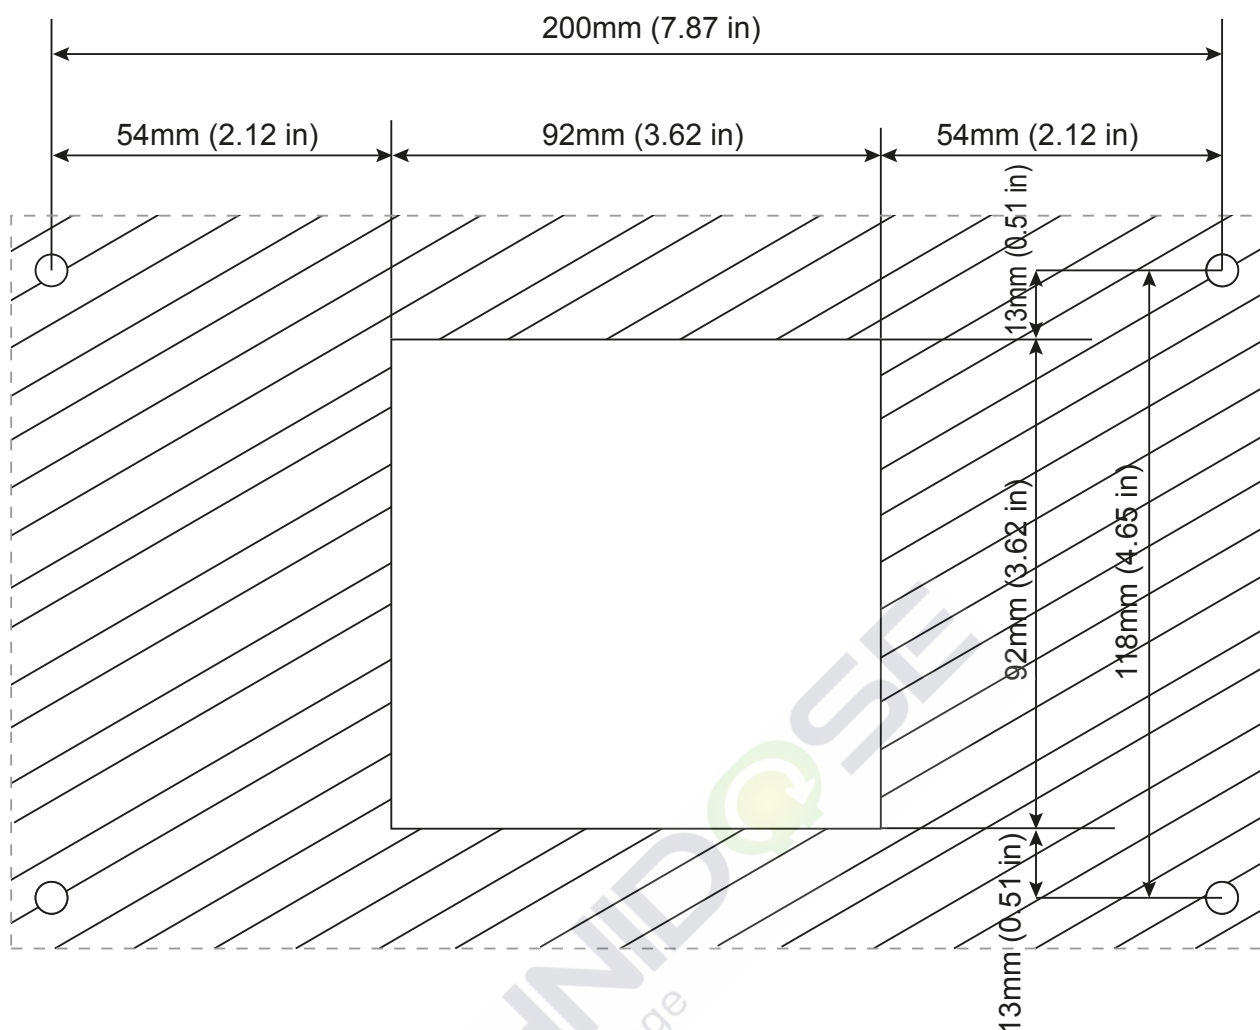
Découpe et dimensions du panneau pour dispositif monté sur panneau
